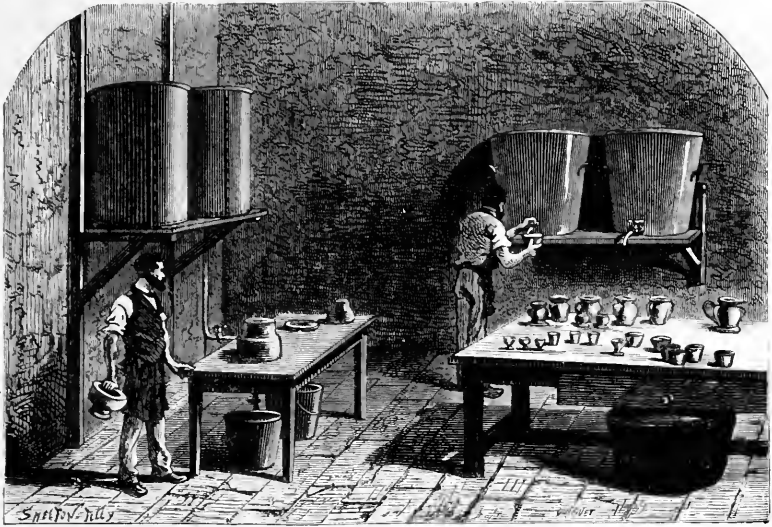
Moulage d'une pièce au moyen de la *barbotine* coulée dans un moule de plâtre. (Dessin pris à la manufacture de Sèvres.)
